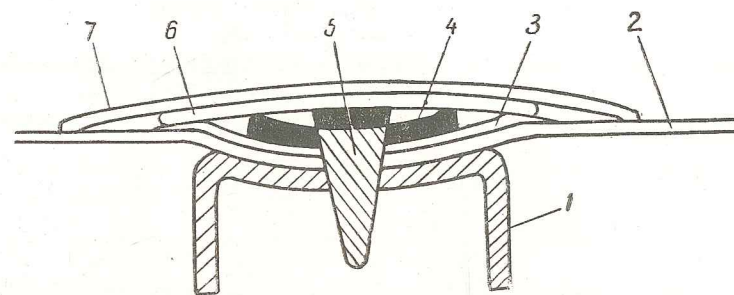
Крепление обшивки винтами к металлическим нервюрам коробчатого сечения:
